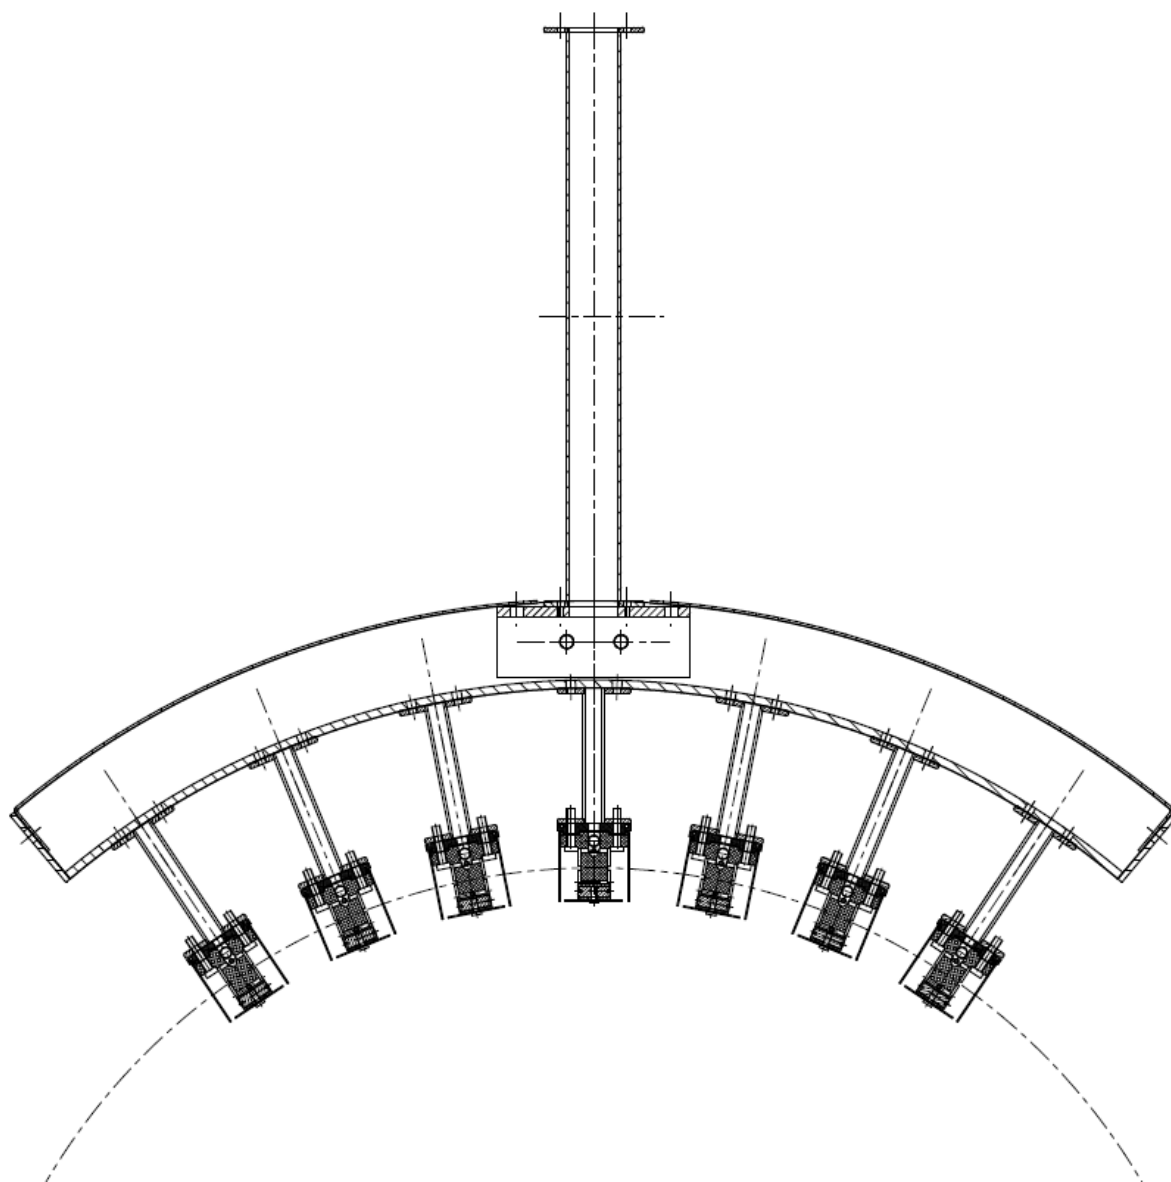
Сборочный чертеж новой магнитной диагностики для ГДЛ
